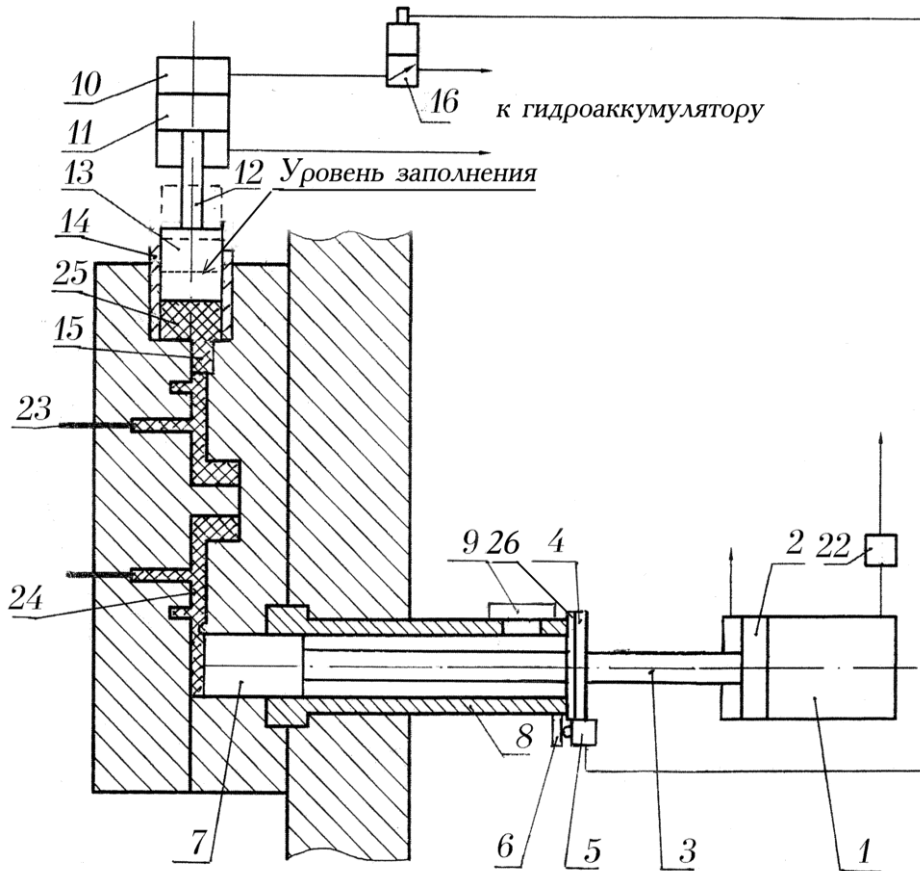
Схема способа литья под давлением с двумя камерами прессования для машин с холодной горизонтальной камерой (конечное положение)
